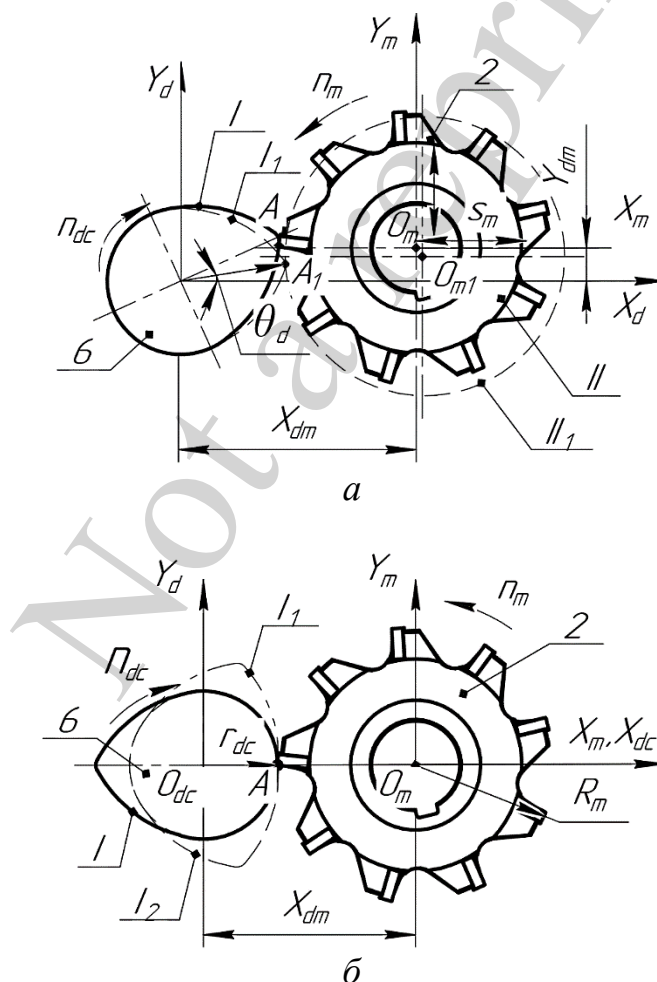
Схема фрезерування ділянок кулачка: а – обробка поверхонь, центри яких не співпадають з центром розподільного валу; б – обробка поверхонь, центри яких співпадають з центром розподільного валу
